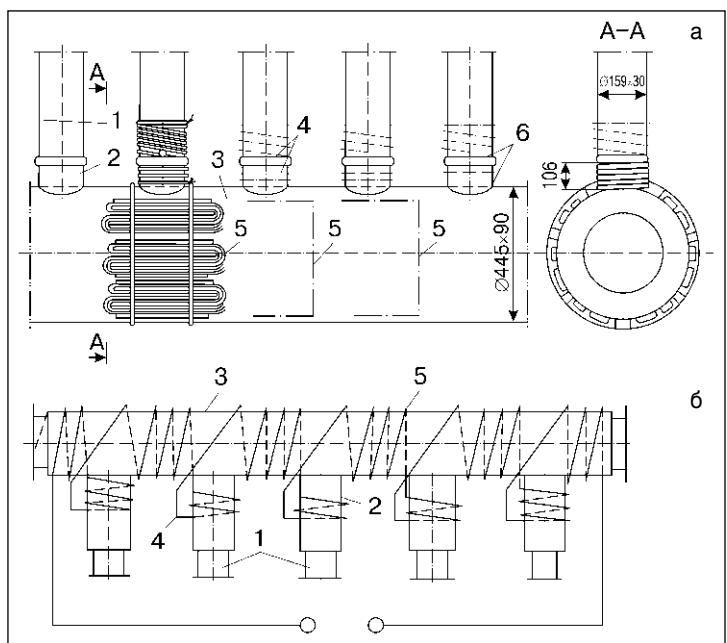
Схемы установки электронагревателей при термообработке сварных соединений труб со штуцерами камер (коллекторами): а — с установкой электронагревателей сопротивления; б — с установкой индукторов (1 — труба; 2 — штуцер; 3 — камера; 4 — электронагреватель на штуцере; 5 — электронагреватель на камере; 6 — сварной шов)
